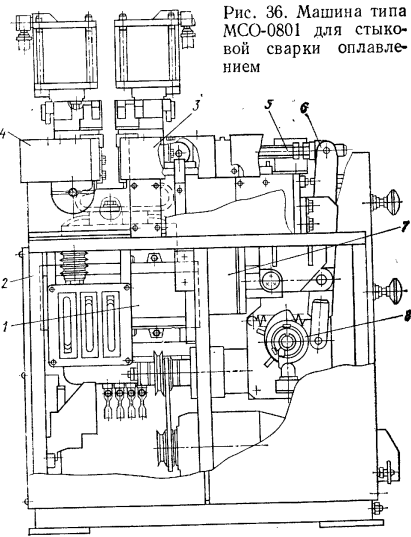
Машина типа МСО-0801 для стыковой сварки оплавлением
